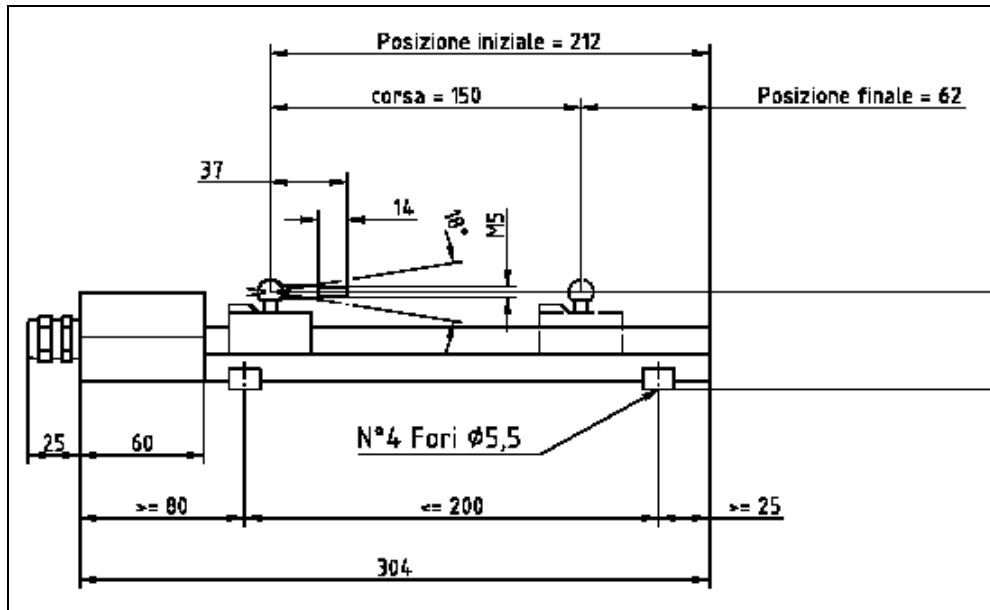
sezione laterale del sistema pistone trasduttore di posizione
